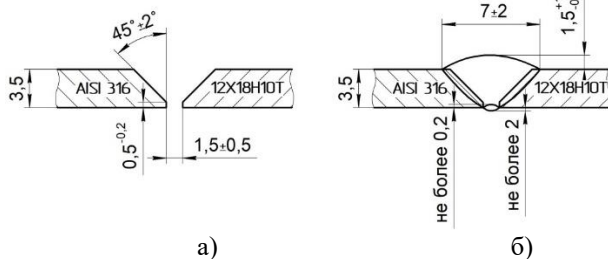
Конструктивные элементы подготовляемых кромок (а) и сварного шва (б)
